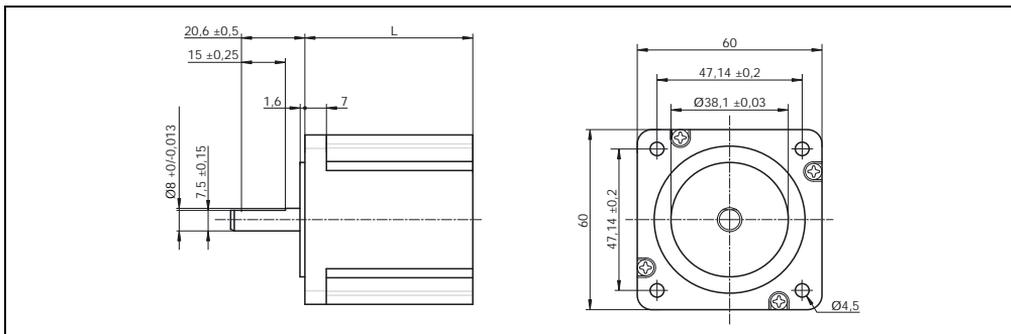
Schrittmotoren Flanschmaß 60 mm - Mechanische Abmessungen
